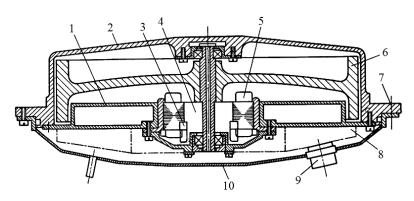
Конструктивная схема бесконтактного двигателя с датчиками Холла: 1 — узел крепления двигателя; 2- кожух маховика; 3 — датчик Холла; 4 — ротор двигателя; 5 — статор двигателя; 6 — маховик; 7 — установочная плоскость; 8 - электронный блок; 9 — штепсельный разъем; 10 — кожух.
